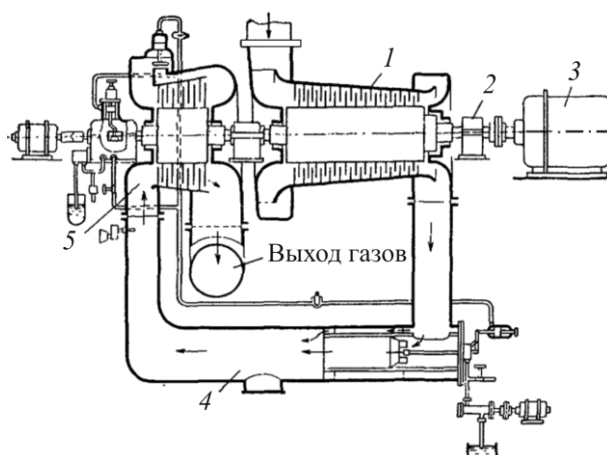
Схема установки осевого компрессора с газовой турбиной
